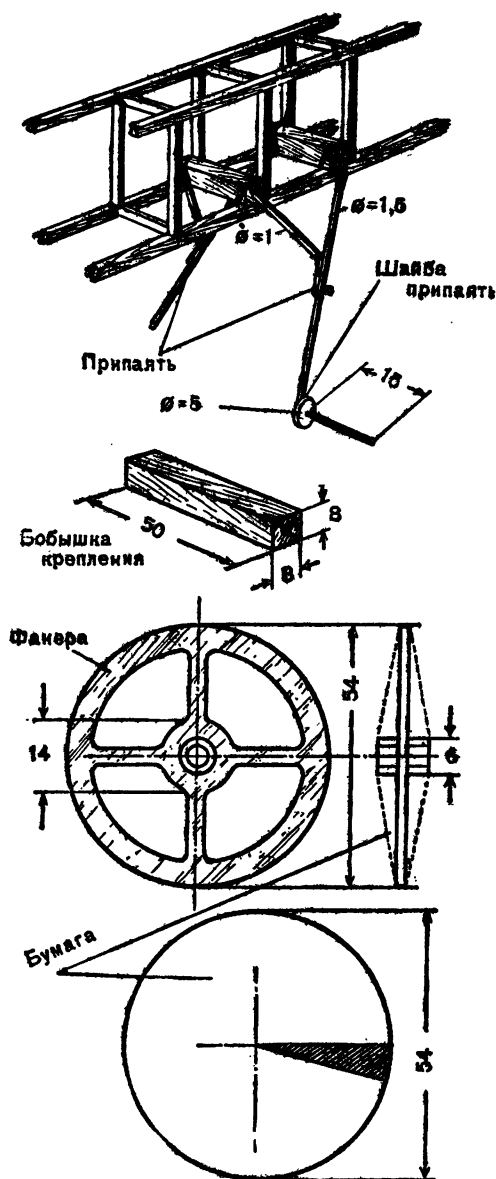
Конструкция шасси, колеса и крепление шасси к фюзеляжу.
